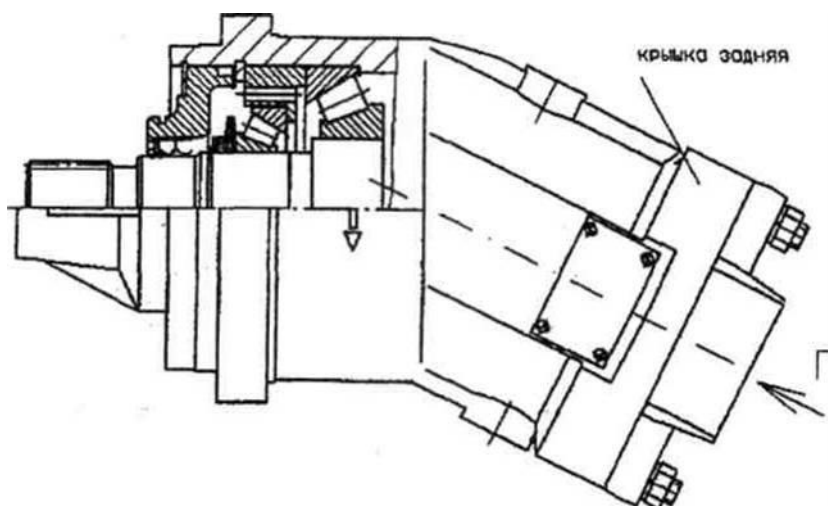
Насос (мотор) с роликовыми коническими подшипниками
